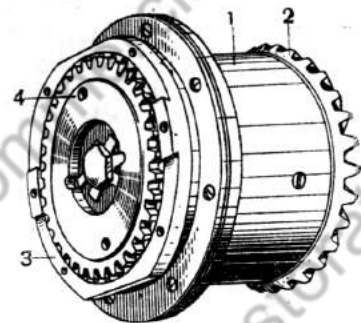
Ведущий вал в сборе: 1 — обойма; 2 — коническая шестерня; 3 — наружная муфта; 4 — зубчатка муфты
